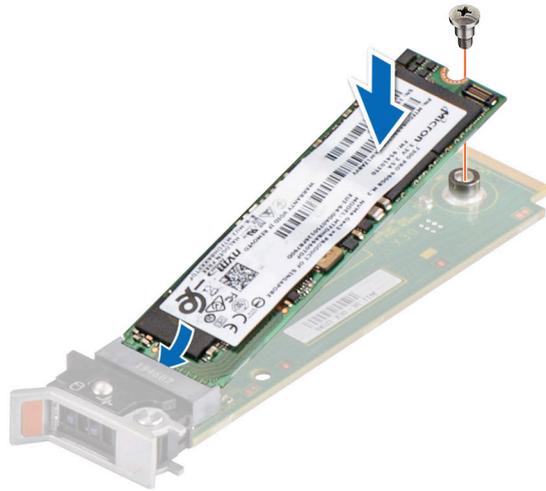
Installieren des M.2-SSD-Laufwerks
